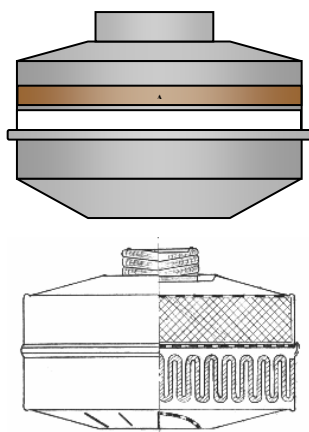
Внешний вид и устройство фильтрующе-поглощающей коробки малого габарита типа А
